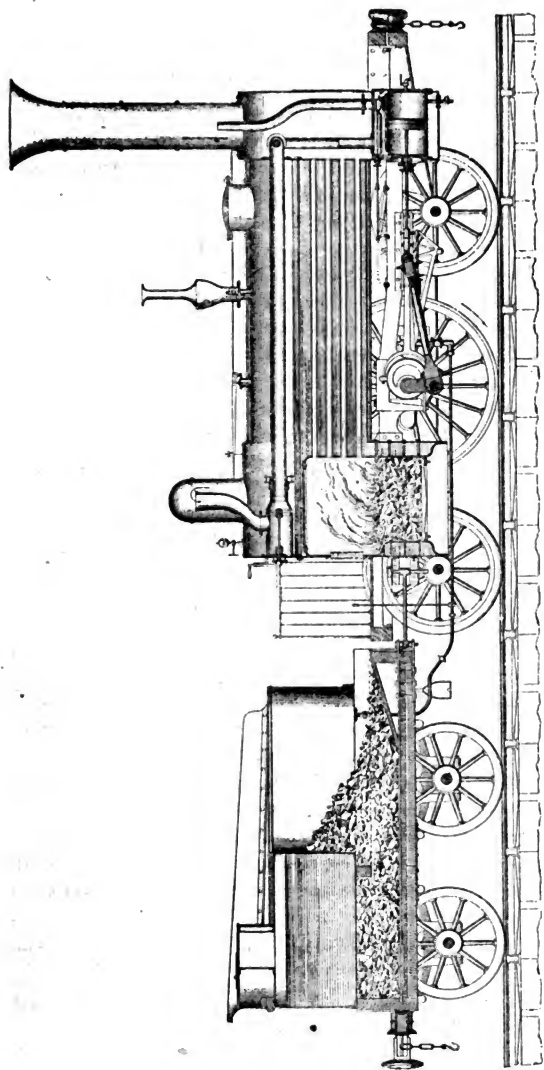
Coupe d'une machine locomotrice et de son tender.
